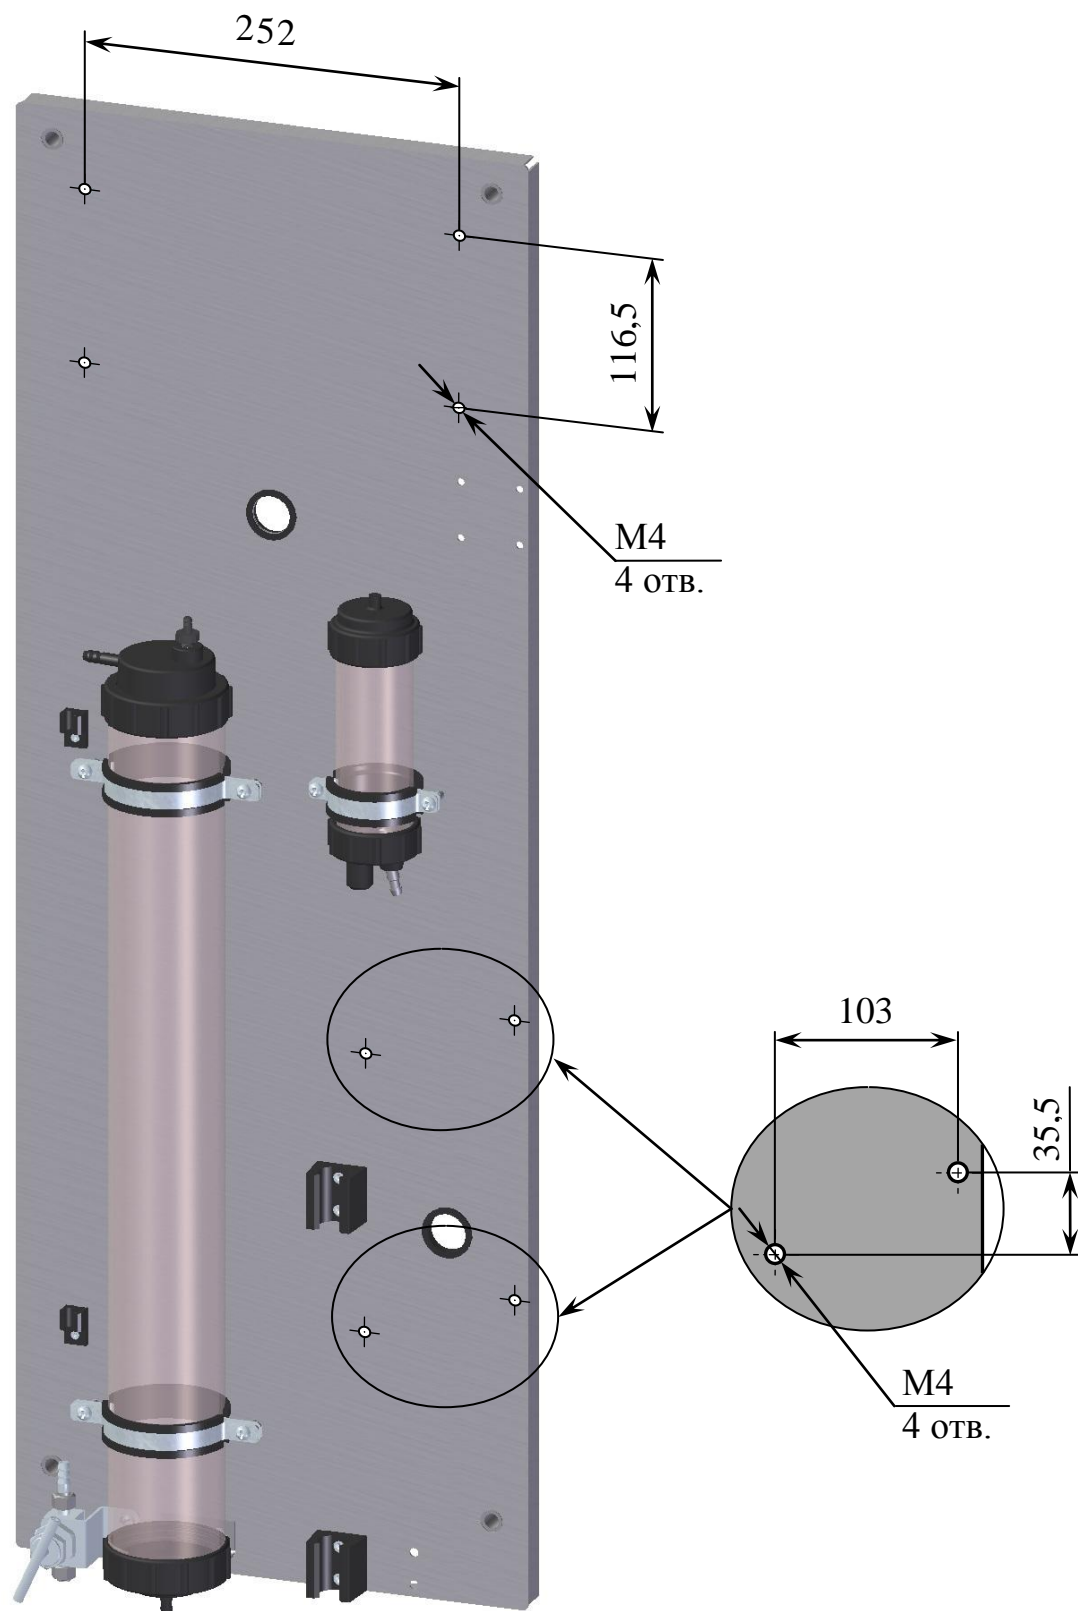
Расположение и размер отверстий на гидропанели для крепления блока преобразовательного и датчиков проводимости
